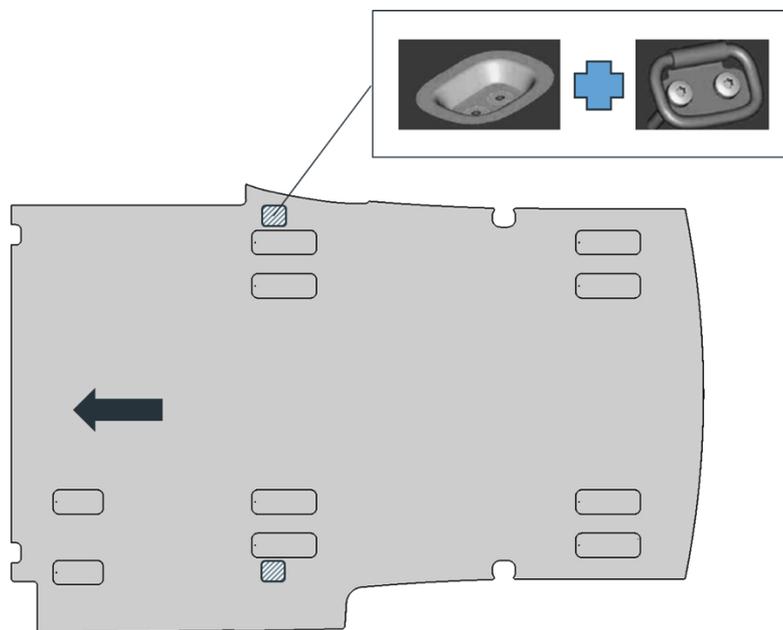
plancher universel (5BM)-Point de fixation en forme de coupelle aux points d'élingage
